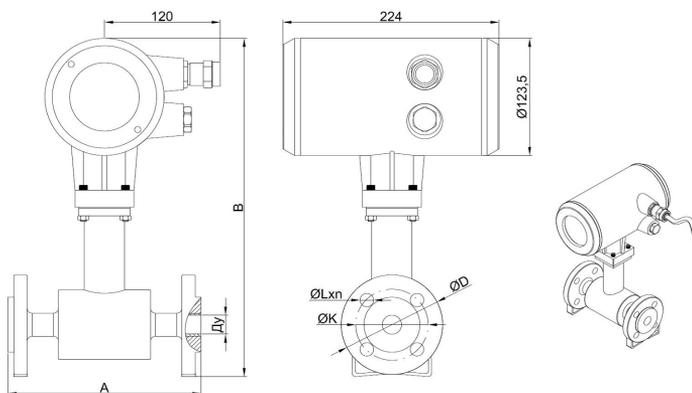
Габаритные размеры взрывозащищенного интегрального исполнения расходомера (корпус 1)
